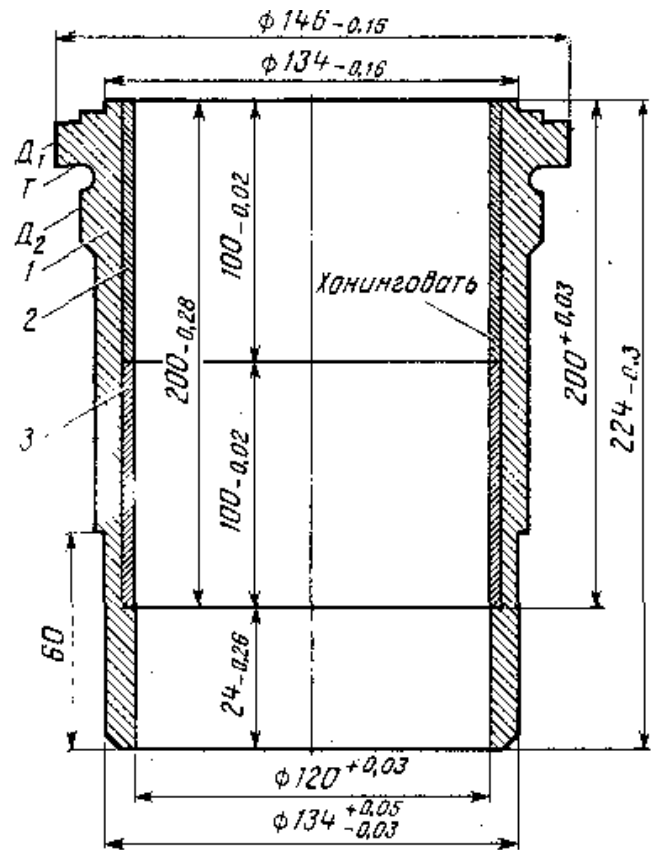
Геометрические размеры гильзы цилиндров КамАЗ-740, восстановленной под номинальный размер:
